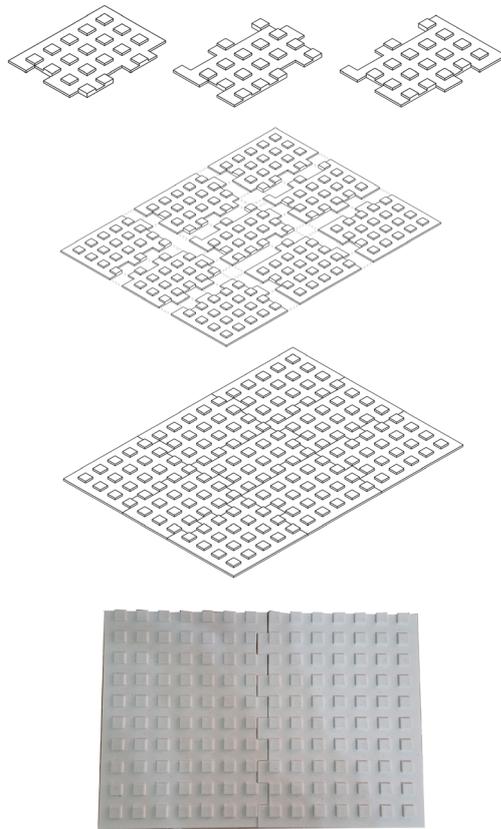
Schema di montaggio del board e conseguente versione prototipale.
